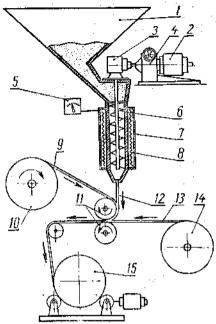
Сварочная машина для сварки тонких листов или пленки расплавленным прутком;
